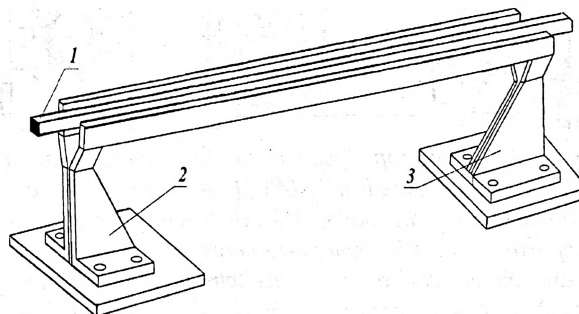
Индуктор для нагрева заготовок чизельного зуба под навивку: 1 — заготовка; 2, 3 — токоподводящие шины индуктора
